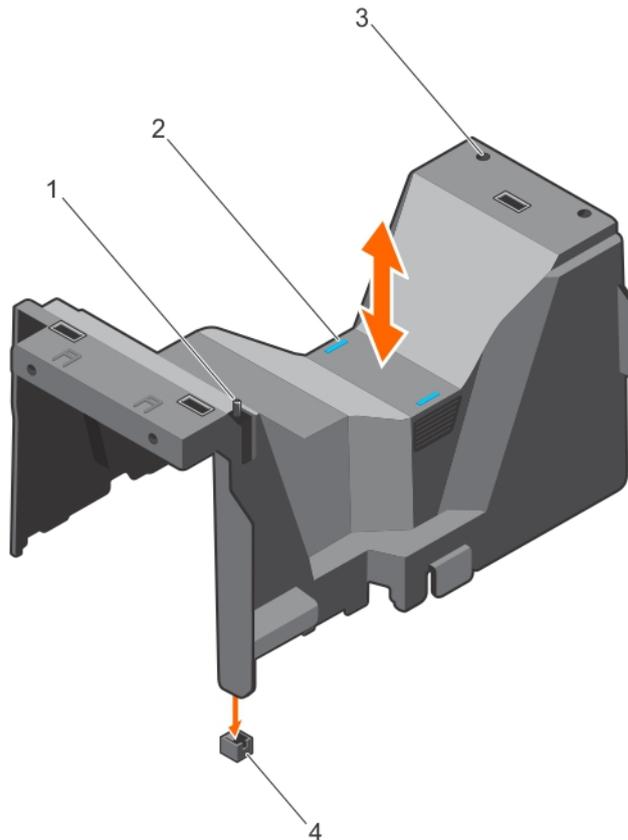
Entfernen und Installieren des Kühlgehäuses – System mit 3,5-Zoll-Festplatten
